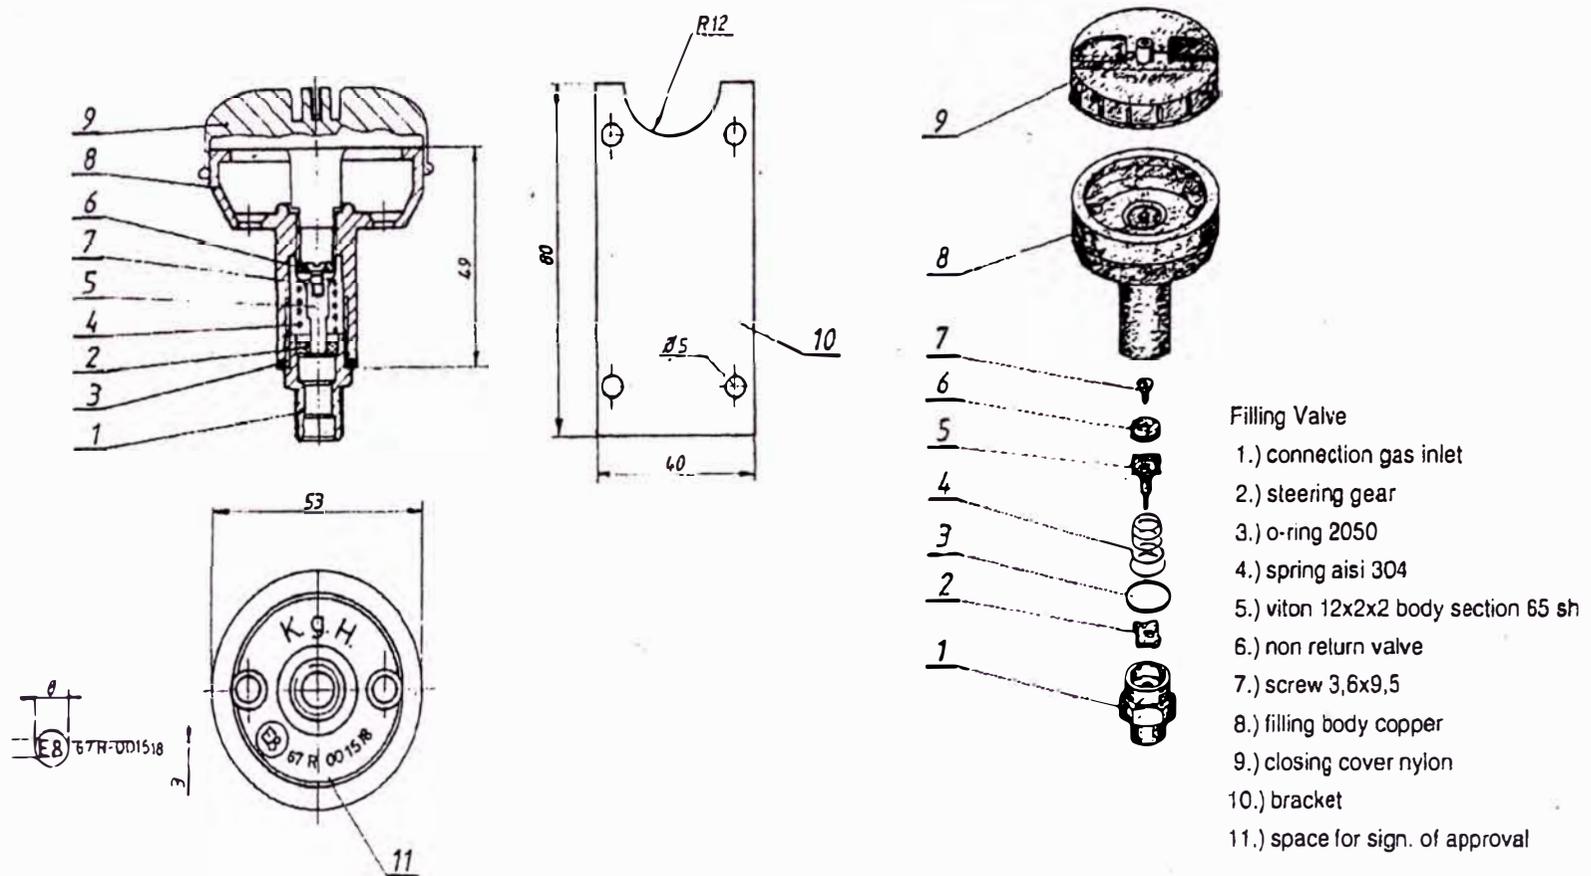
Componentes que constituyen la válvula remota de llenado
